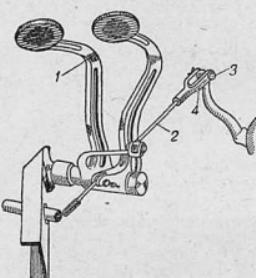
Привод механизма сцепления автомобиля ГАЗ-М-1
